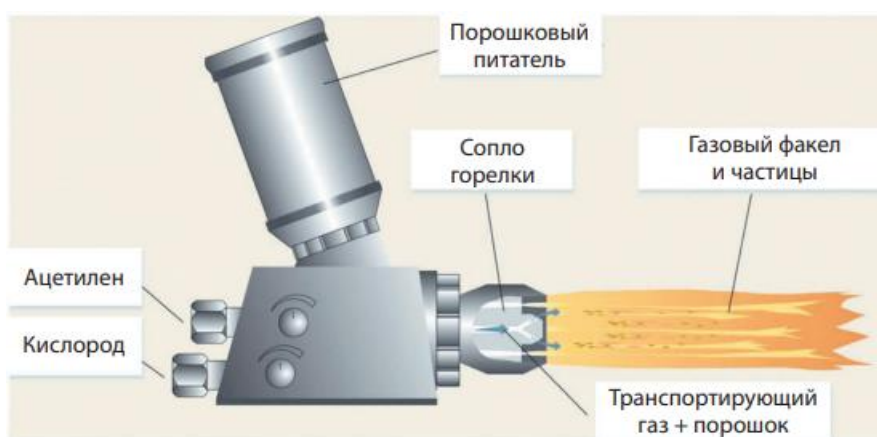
Схема горелки для газопламенного порошкового напыления
